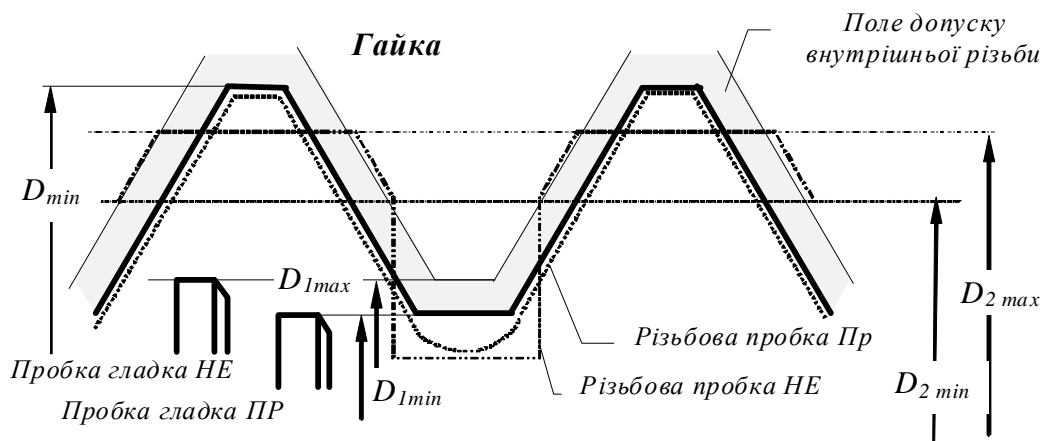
Схема перевірки різьби гайки калібрами
